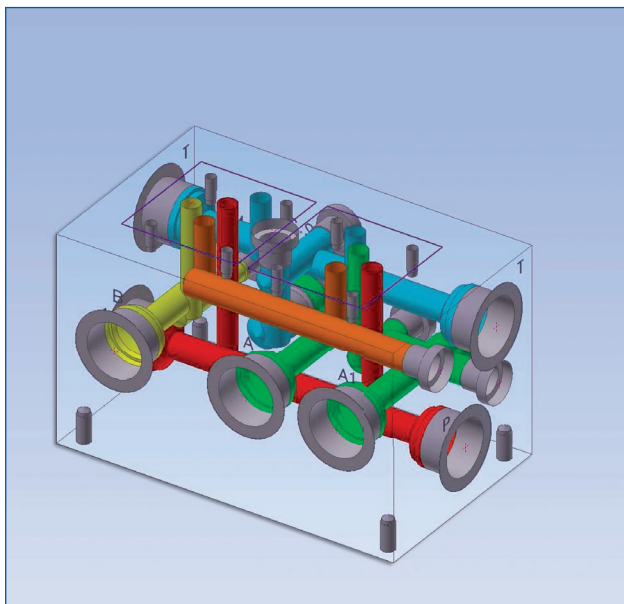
Hydraulik-Steuerblock aus Strangguss Gusseisen mit Kugelgraphit
